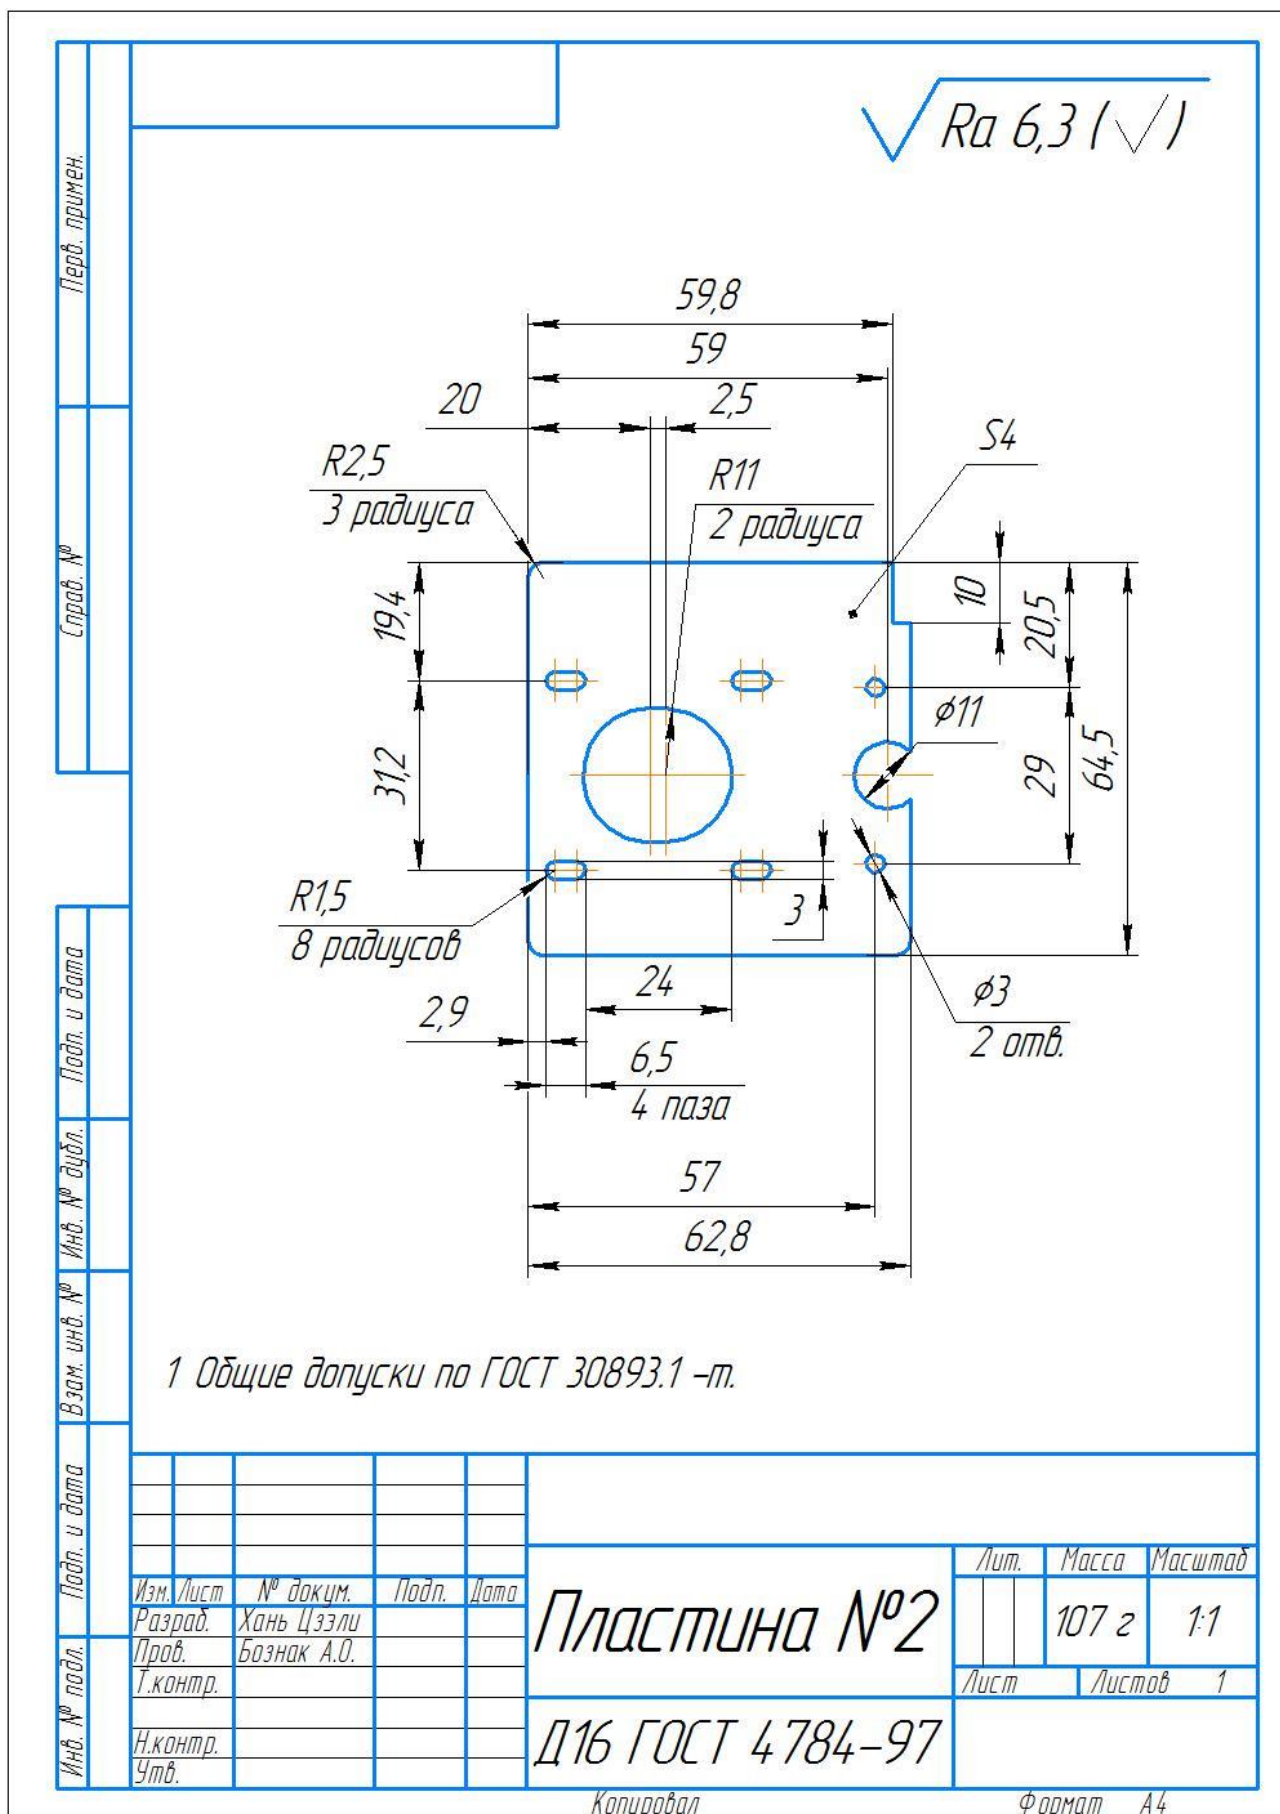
Чертеж детали «Пластина №2»
